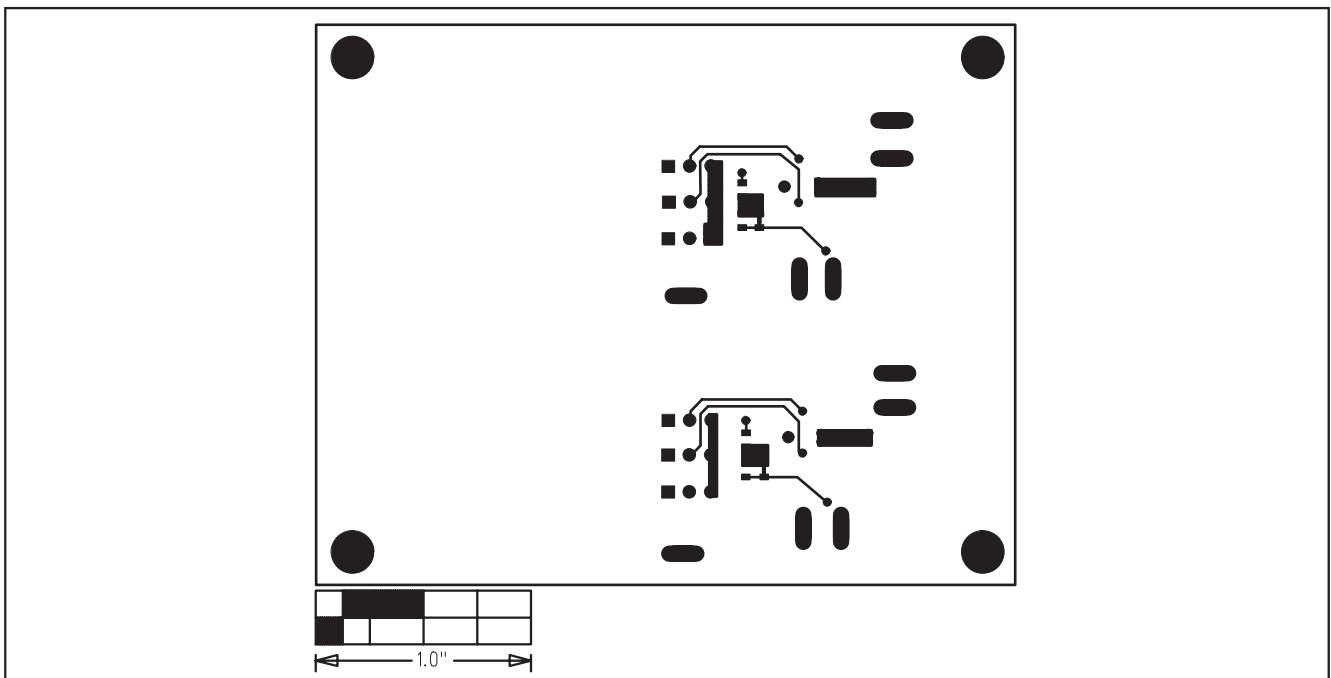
MAX1556 评估板 PCB 布局图 — 焊接面
